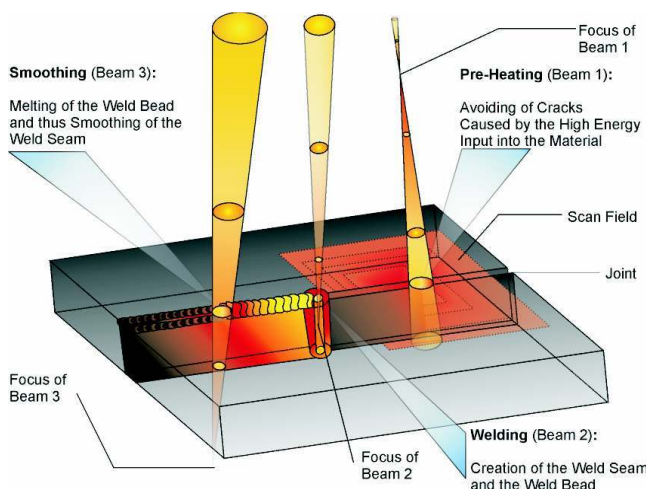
Vorwärmen, Schweißen und Glätten mit der Mehrstrahltechnik
